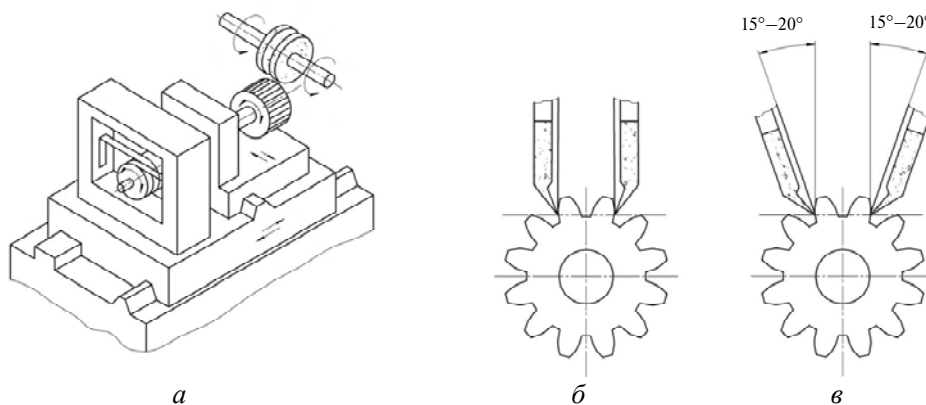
Схема шлифования зубчатых колес непрерывной обкаткой двумя тарельчатыми кругами (а) и расположение шлифовальных кругов относительно обрабатываемого колеса под углом 0 (б) и $15^\circ\text{--}20^\circ$ (в).
